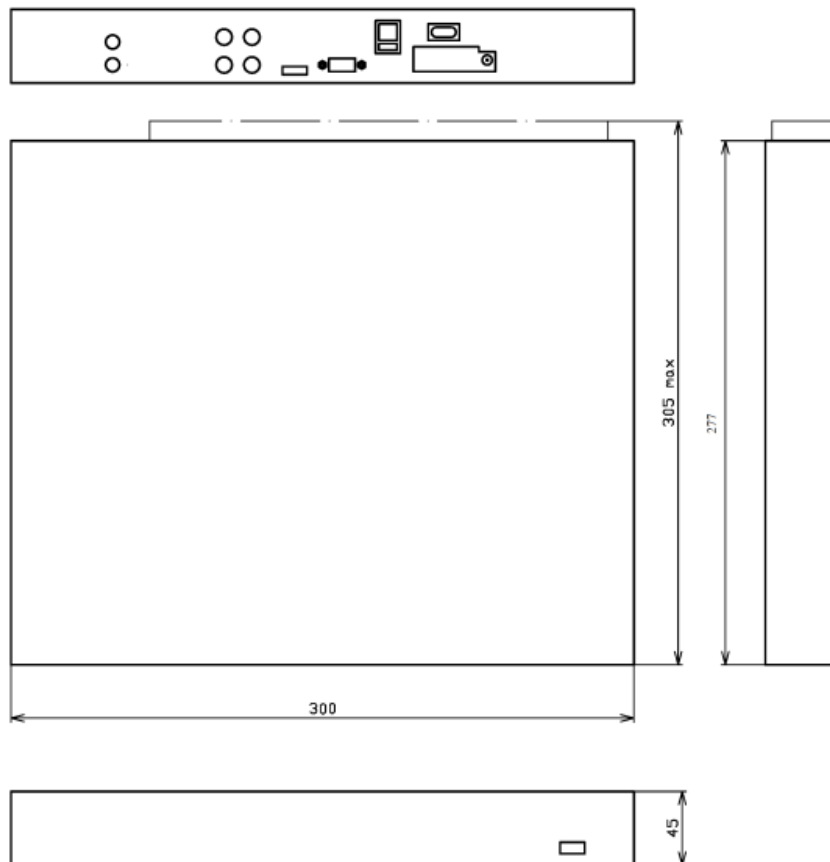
Габаритный чертеж ИВМ-8004
